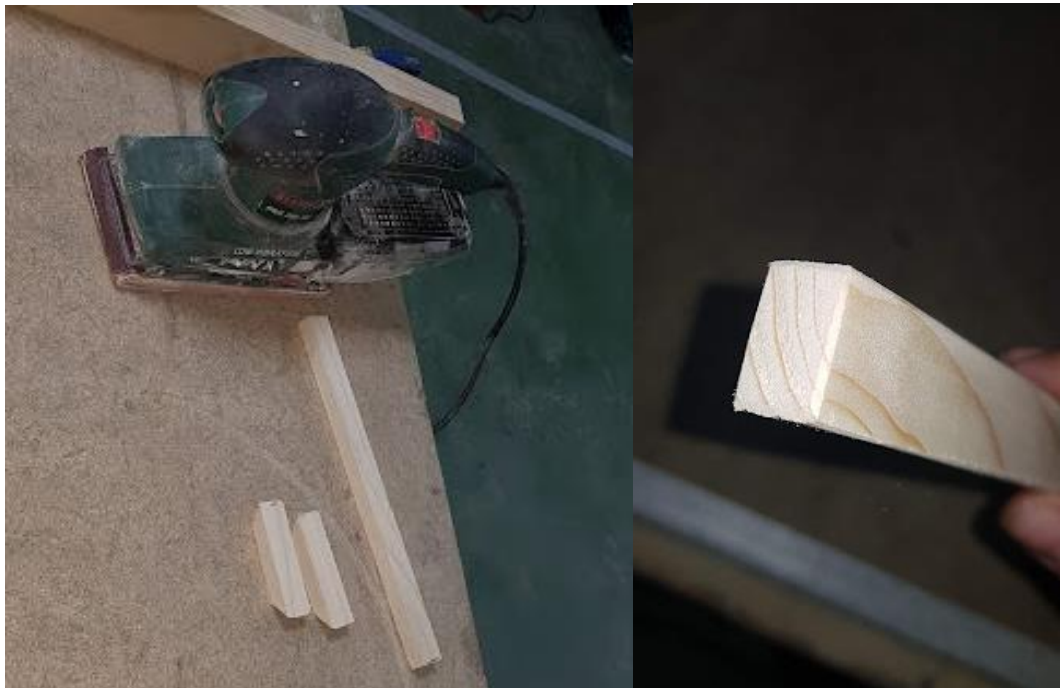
Lijado de listones de madera. Fuente: Elaboración propia
